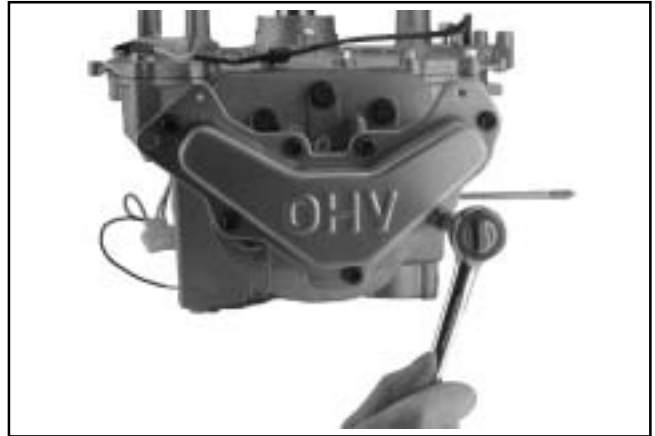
Desmontaje de los tornillos de la tapa de la válvula.
